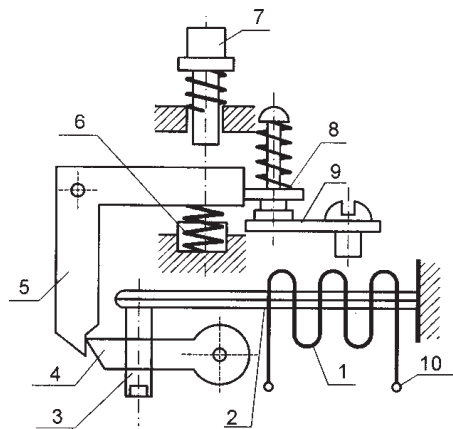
Схема теплового реле: 1 — нагреватель; 2 — биметаллическая пластинка; 3 — регулировочный винт; 4 — защелка; 5 — рычаг; 6 — пружина; 7 — кнопка возврата; 8 — подвижный контакт; 9 — неподвижный контакт; 10 — вывод нагревателя.
